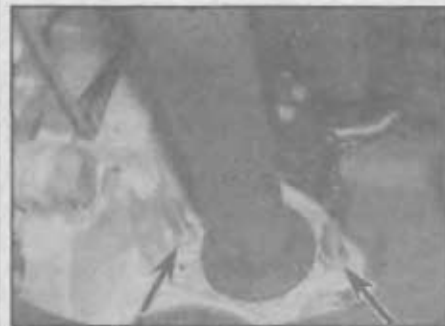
Расположение гаек крепления промежуточного подшипника правого приводного вала
